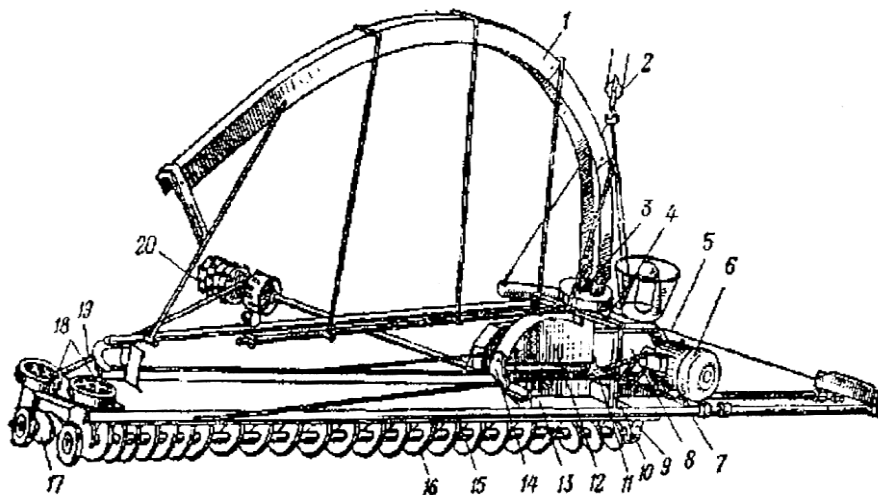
Конструктивна схема розвантажувача башт: 1 – дефлектор; 2 – блок підвіски; 3 – струмознімач; 4 – трикутна підвіска; 5 – трос; 6 – електродвигун; 7 – рама; 8 – кожух; 9 – редуктор; 10, 13 – щитки; 11 – натяжний пристрій; 12 – шпурлялка; 14 – кронштейн;
